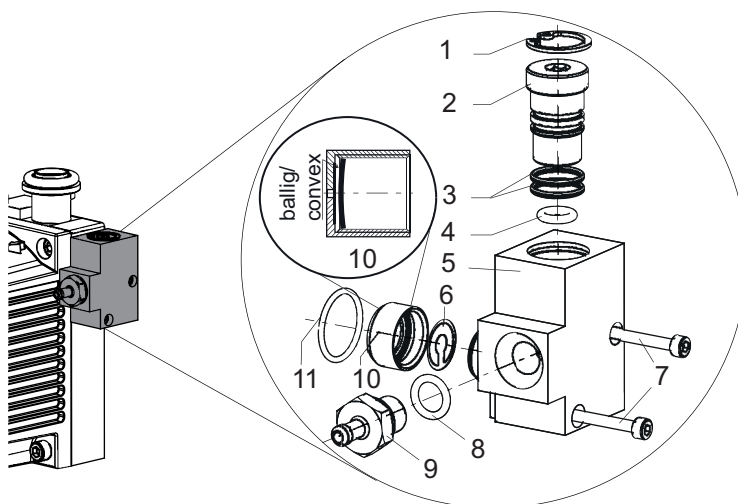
Valvola gas zavorra con attacco per gas di lavaggio
